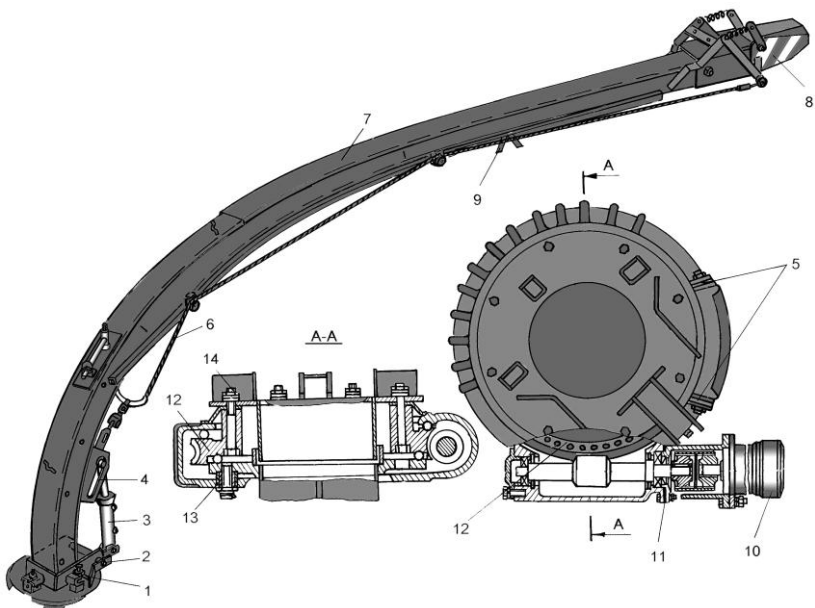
Силосопровод: 1 – болт; 2 – ось; 3 – гидроцилиндр; 4 – кронштейны; 5 – болты крепления; 6 – трос; 7 – желоб; 8 – козырек; 9 – ловители; 10 – гидромотор; 11 – крепление гидромотора; 12 – червячный редуктор; 13 – втулки; 14 – спецболты
